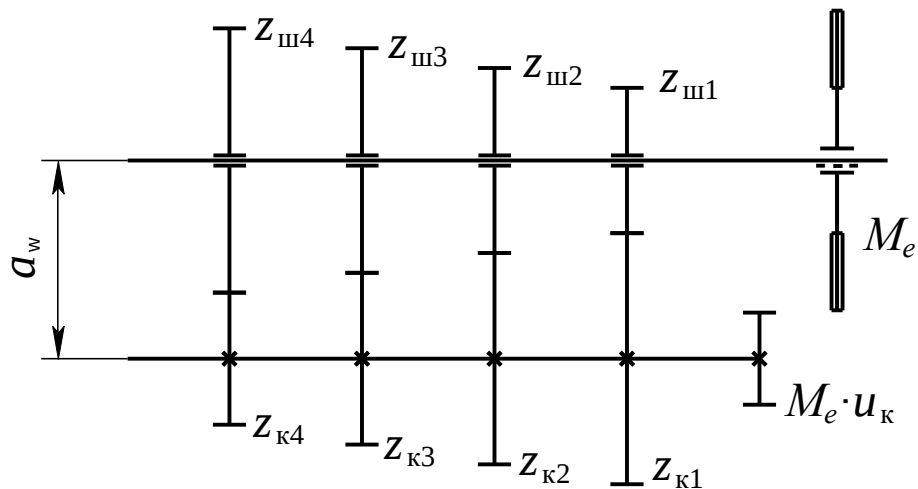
Розрахункова схема двовальної коробки передач:
